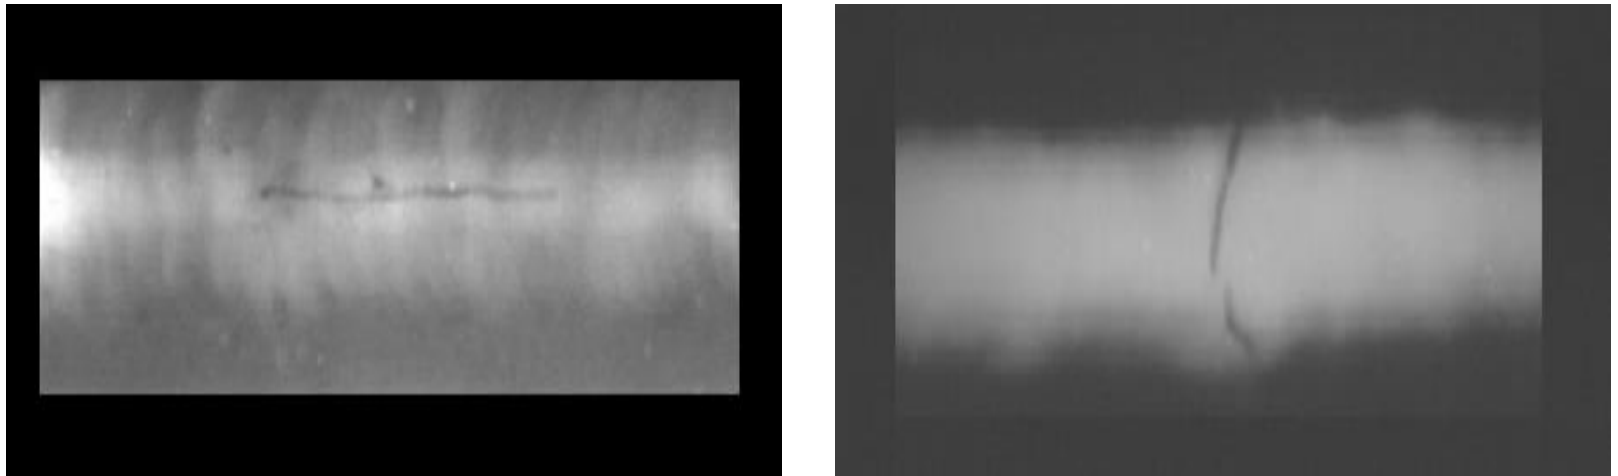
Radiografías de cordones de soldadura defectuosos.
